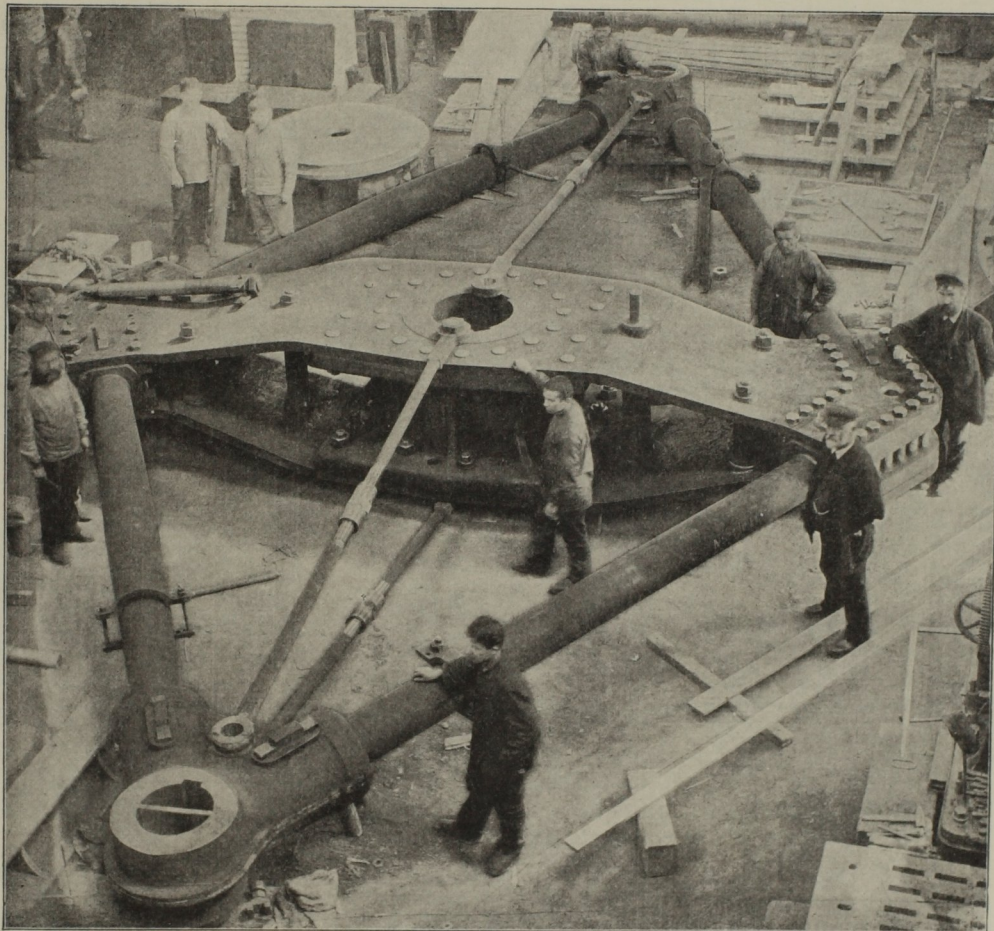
Schwinge einer grossen Wasserhaltungsmaschine,
